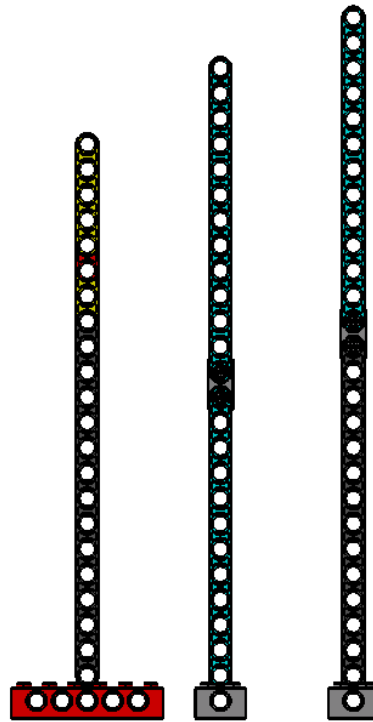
Pilar lateral (1), pilar intermedio (2) y pilar central (3) del pórtico en CATIA v5
